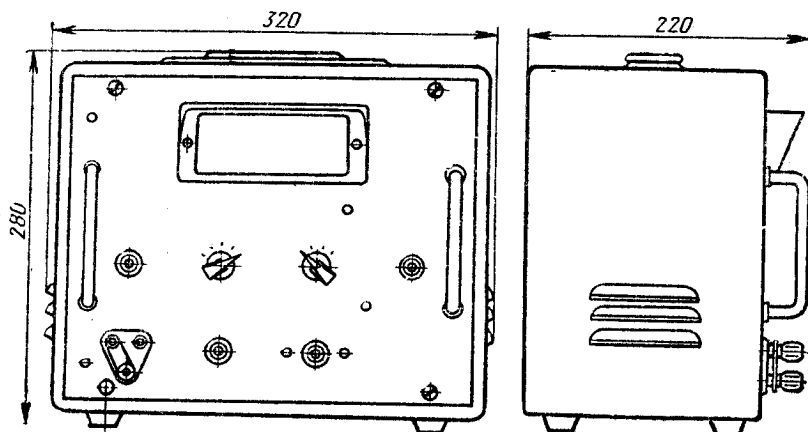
Габаритный чертеж прибора типа В2-9.
